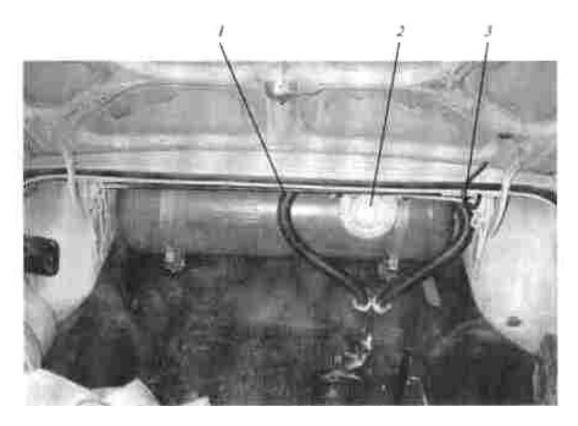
Расположение баллона СНГ с арматурой в багажнике: $1\ u\ 3-$ вентиляционные трубки; 2- корпус мультиклапана с крышкой.
